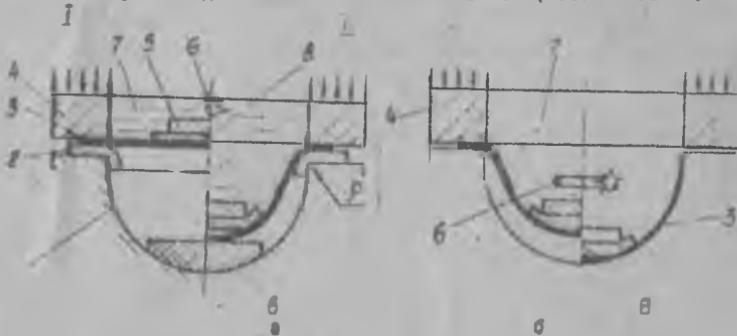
Рис. I. Способ взрывной штамповки тонкостенных крупногабаритных деталей: 1-матрица; 2-сменные матричные кольца; 3-заготовка (деталь, рис. II); 4-применяющее кольцо; 5-экран; 6-заряд взрывчатого вещества; 7-передающая среда; 8-эластичные шайбы.
